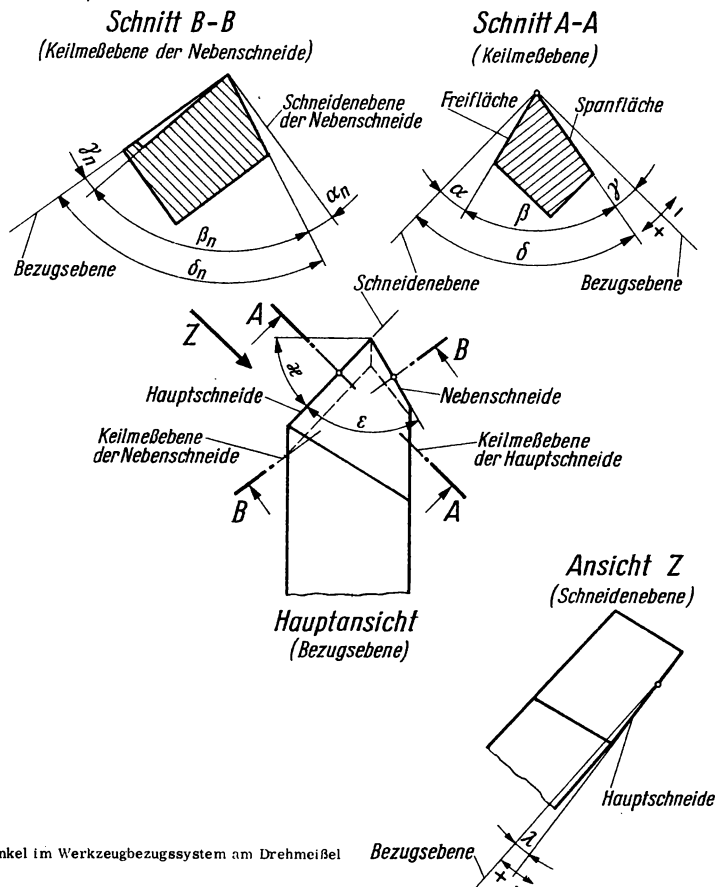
Winkel im Werkzeug Bezugssystem am Drehmeißel
